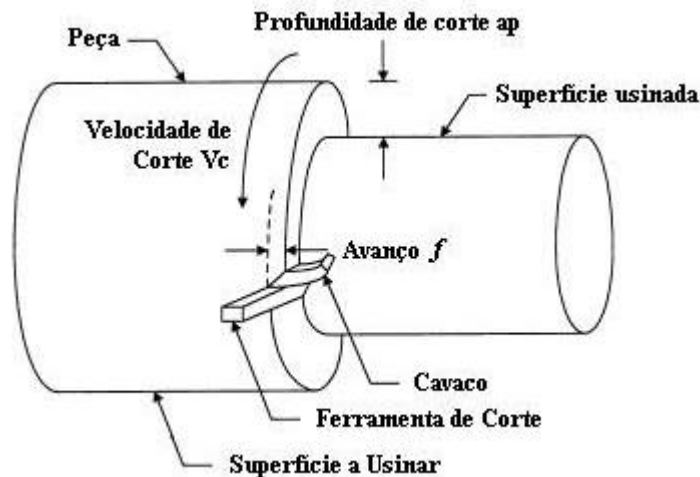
Parâmetros de corte e superfícies em torneamento cilíndrico externo.
